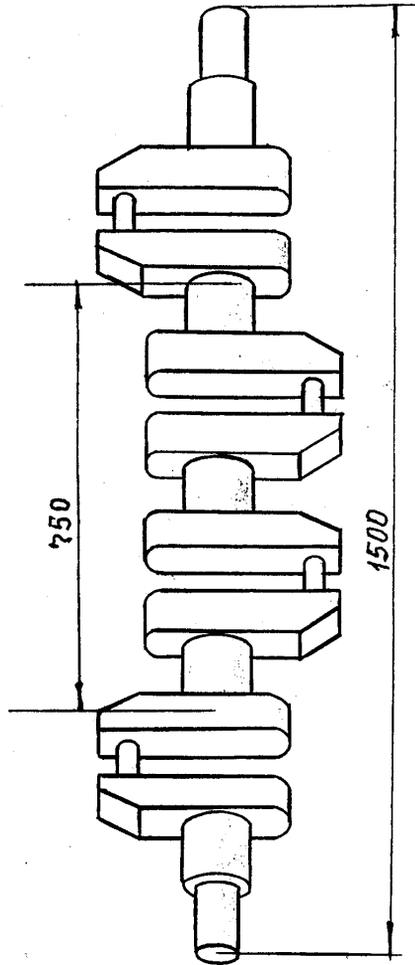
Коленчатый вал двигателя легкового автомобиля
